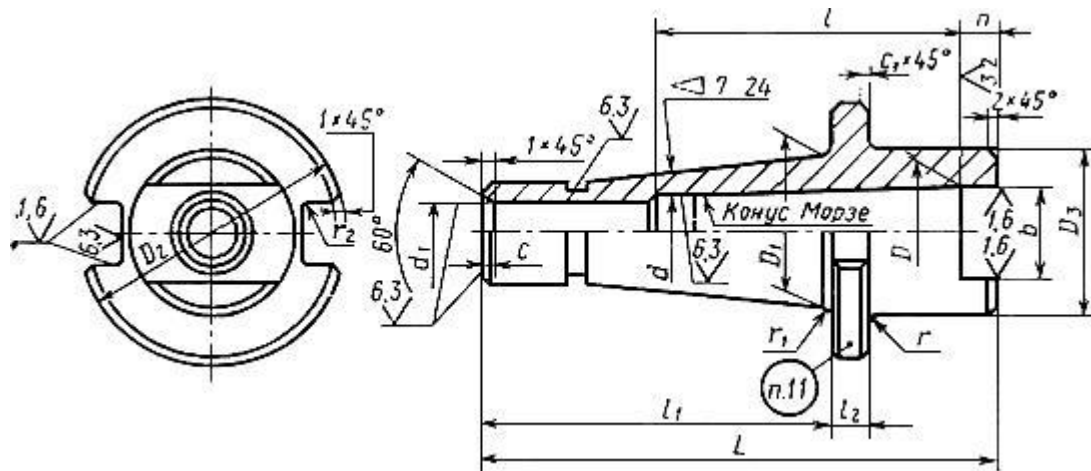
Оправка інструментальна (Tool holder)
